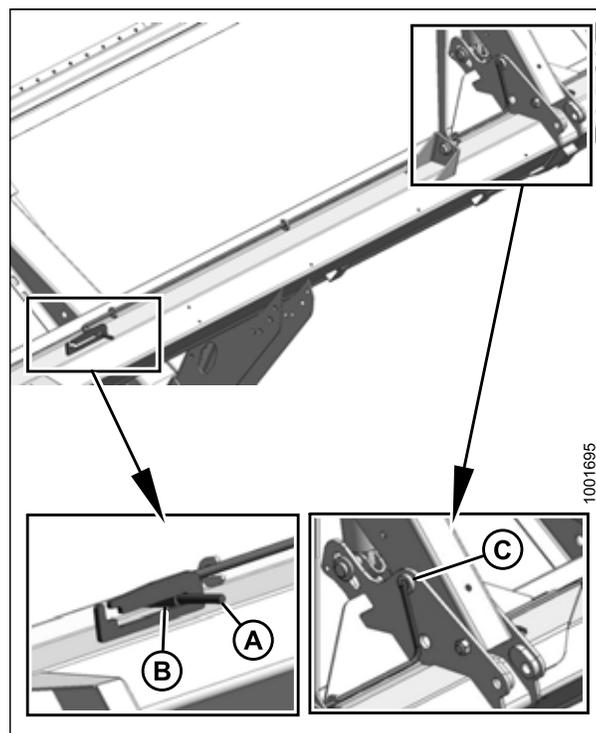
Предохранительный упор подбирающего мотовила — центральный рычаг
